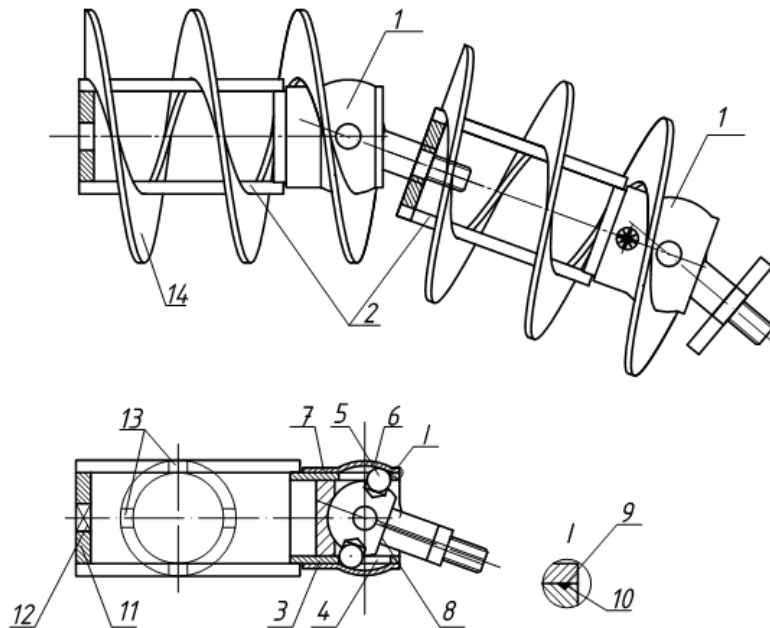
Конструкція гвинтового шарнірного секційного робочого органу
